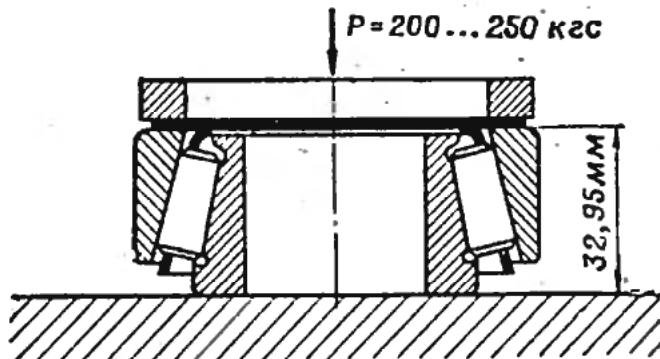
Замер монтажной высоты подшипника ведущей шестерни главной передачи
